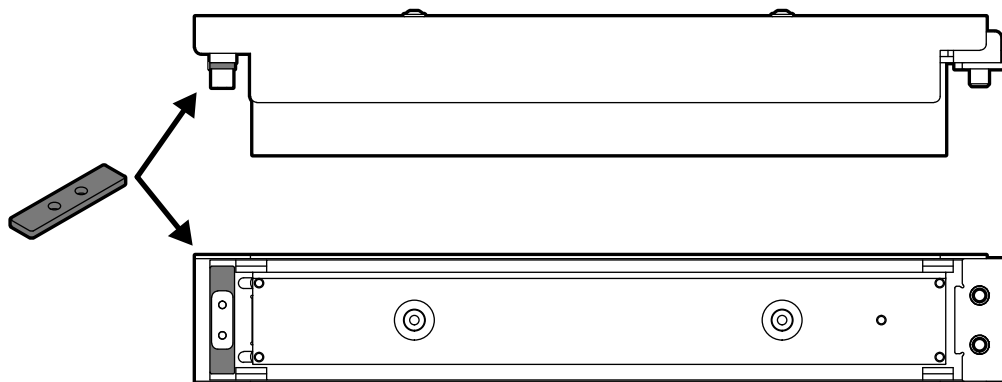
Przykręć Recoater blade z podkładką łożyska liniowego I do łożyska.
